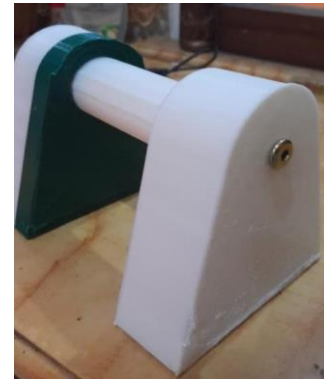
Hasil Pencetakan Kaki Parallette pada 3D Printer
